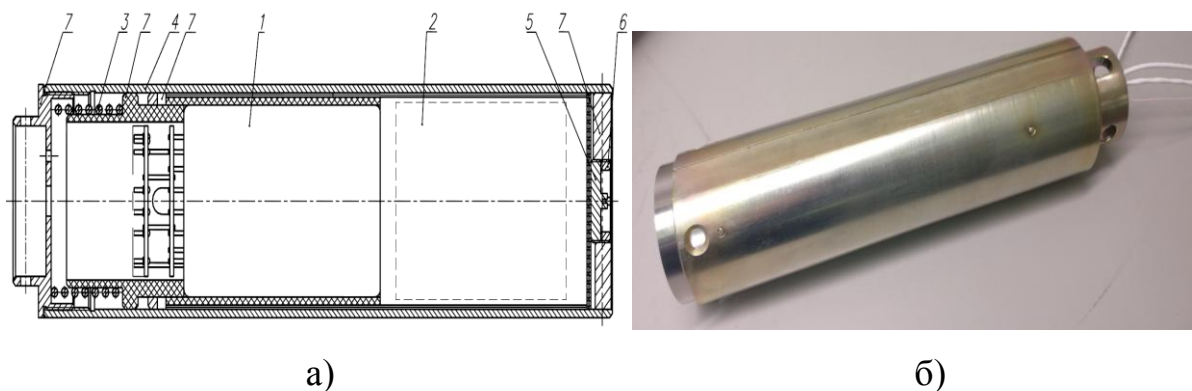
Блок детектора прибора ИНГКС с магнитной защитой а) - конструкция: 1 – ФЭУ, 2 – сцинтилляционный кристалл, 3- пружина, 4 – корпус, 5 – винт, 6 – гайка, 7 – втулки; б) – внешний вид
